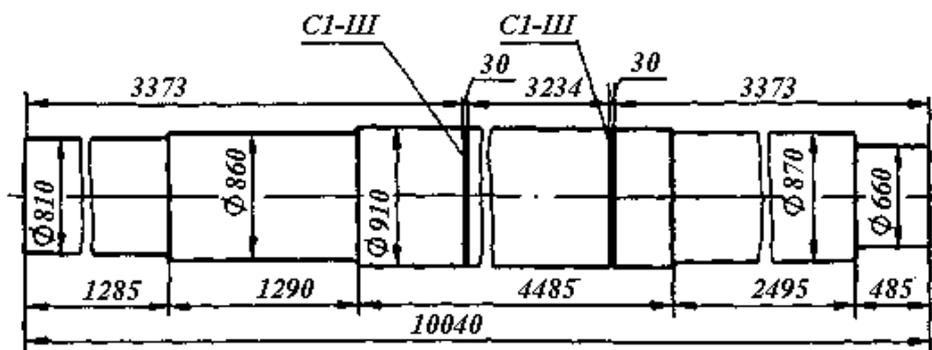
Сварной вал шахтной подъемной машины
